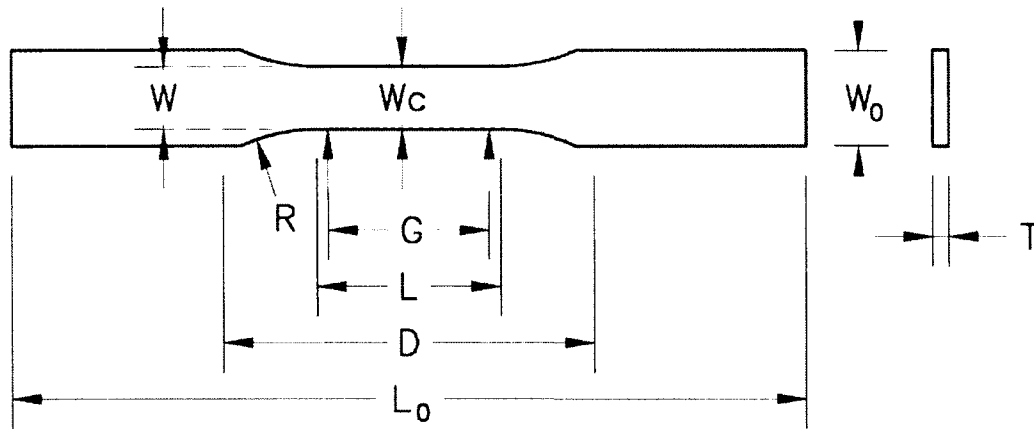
Forme des éprouvettes selon la norme ASTM D 638 – 03
